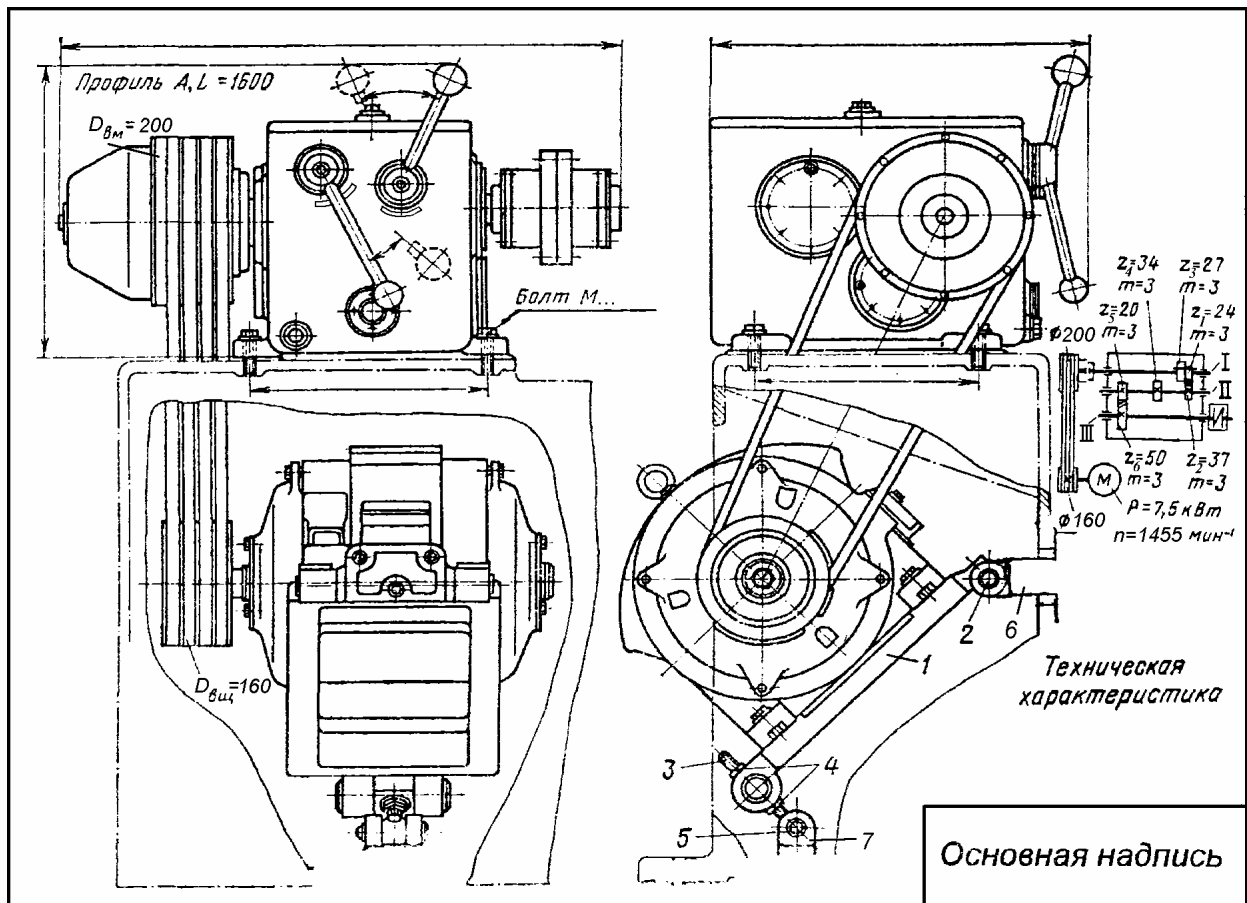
Общий вид привода токарного станка с установкой на станине
